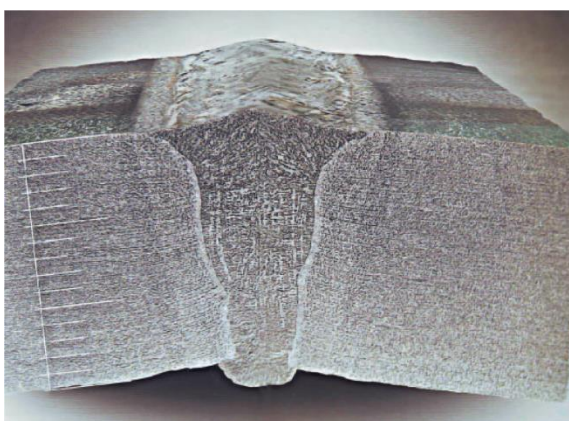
Образец толщиной 15мм (сварка за один проход) [14]
